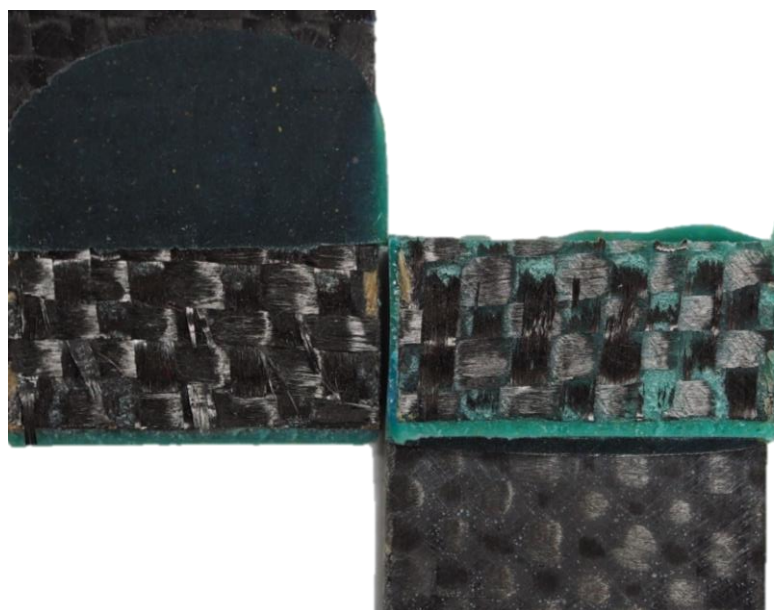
Superfície de ruptura das juntas colada do AC2 - BETAMATE 2096
